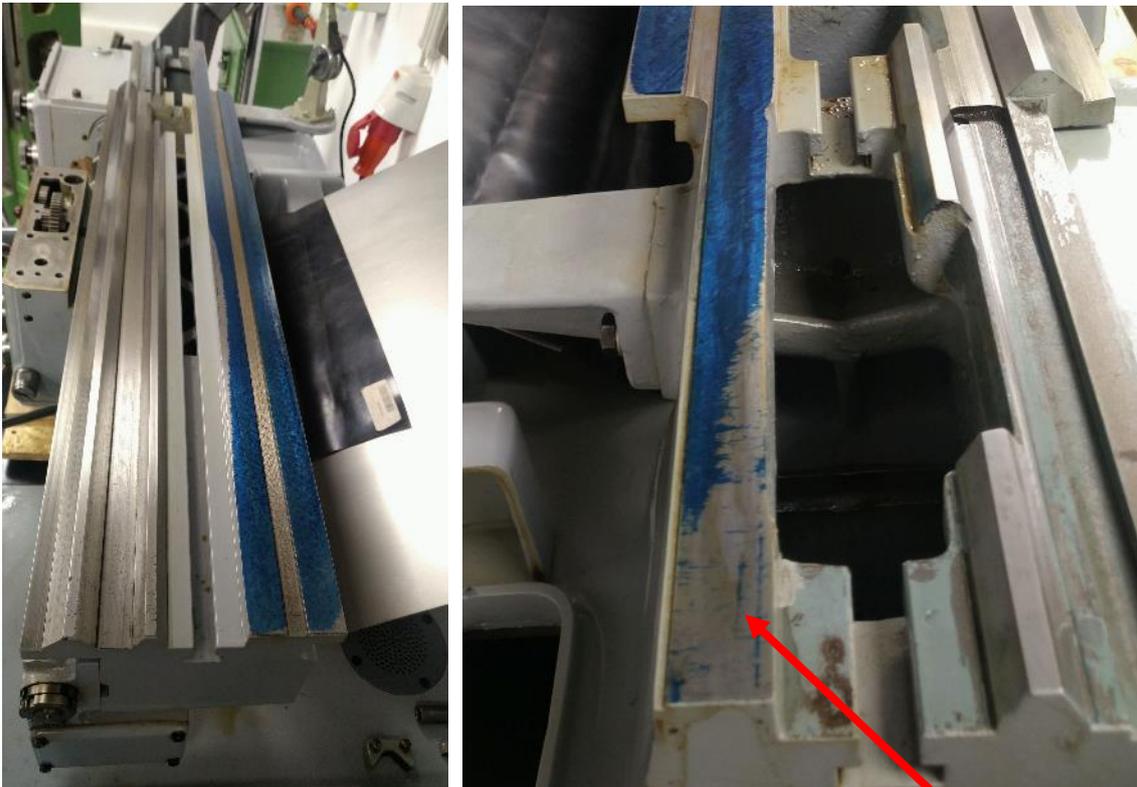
links: Tuschierbild der Flachführung; rechts: unter dem Spindelstock ● kippt die Fläche jedoch ab!
